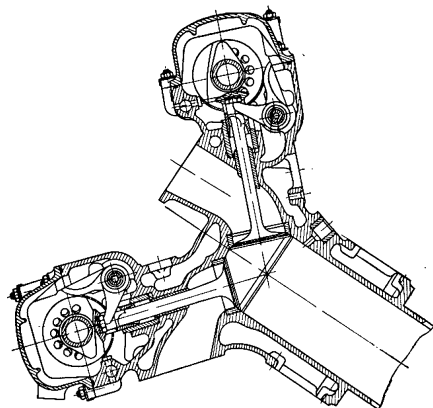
Головка блока и верхняя часть двигателя «Мерседес-Бенц»
